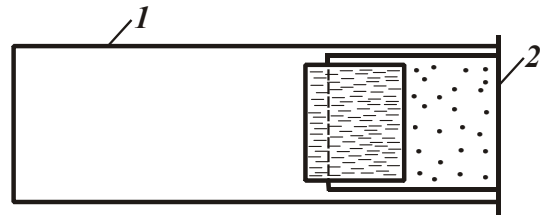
Абразивно-шлифовальная обработка цилиндров с помощью патронов: 1 – обрабатываемый цилиндр; 2 – патрон.
